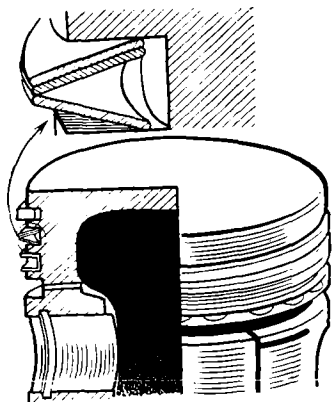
Размещение поршневых колец в канавках поршня двигателя легкового автомобиля
